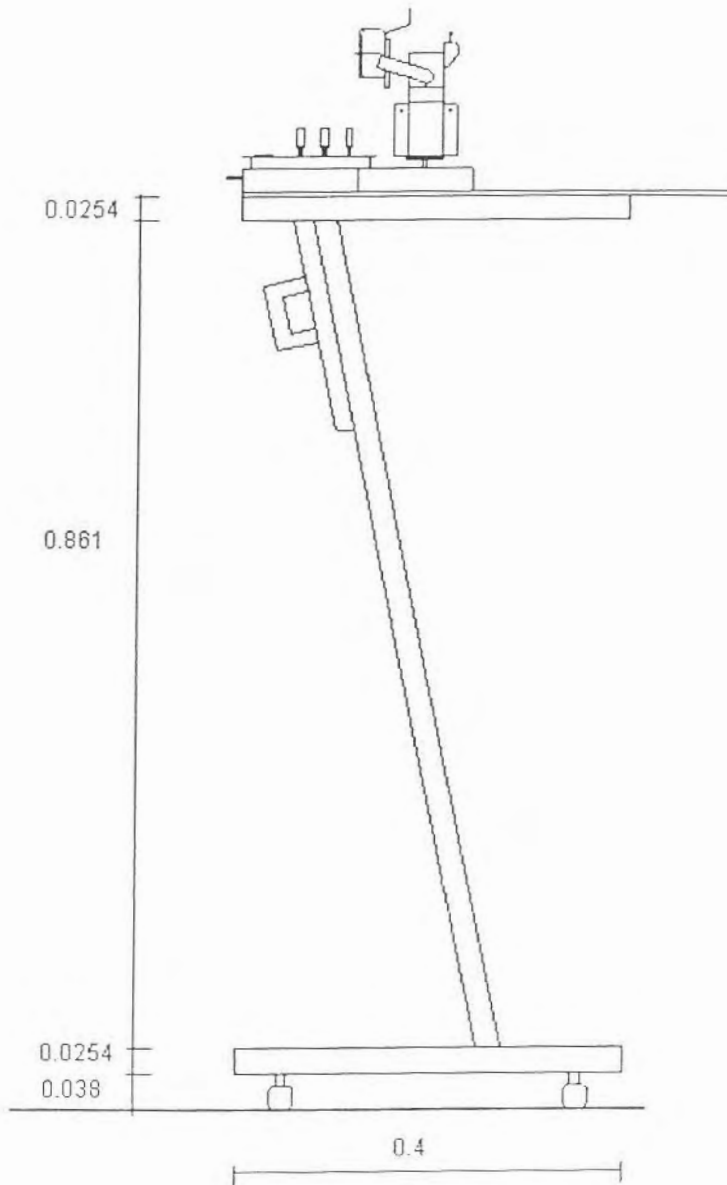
Vista lateral izquierda del soporte del brazo robot
